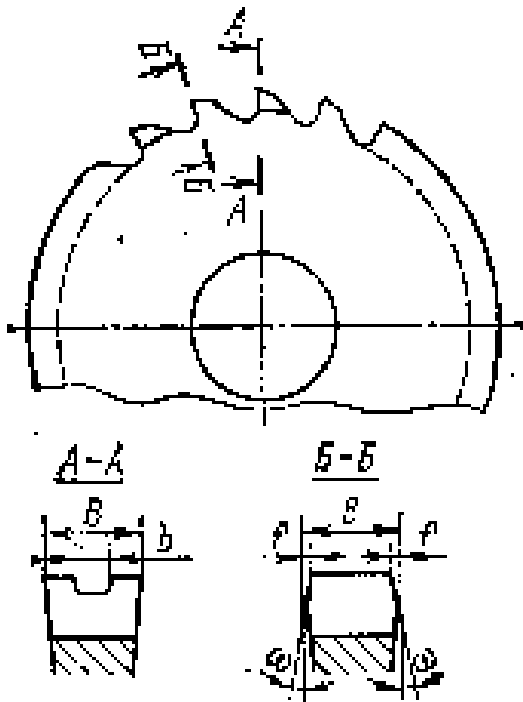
Відрізна фреза з розділовими канавками на зубах
